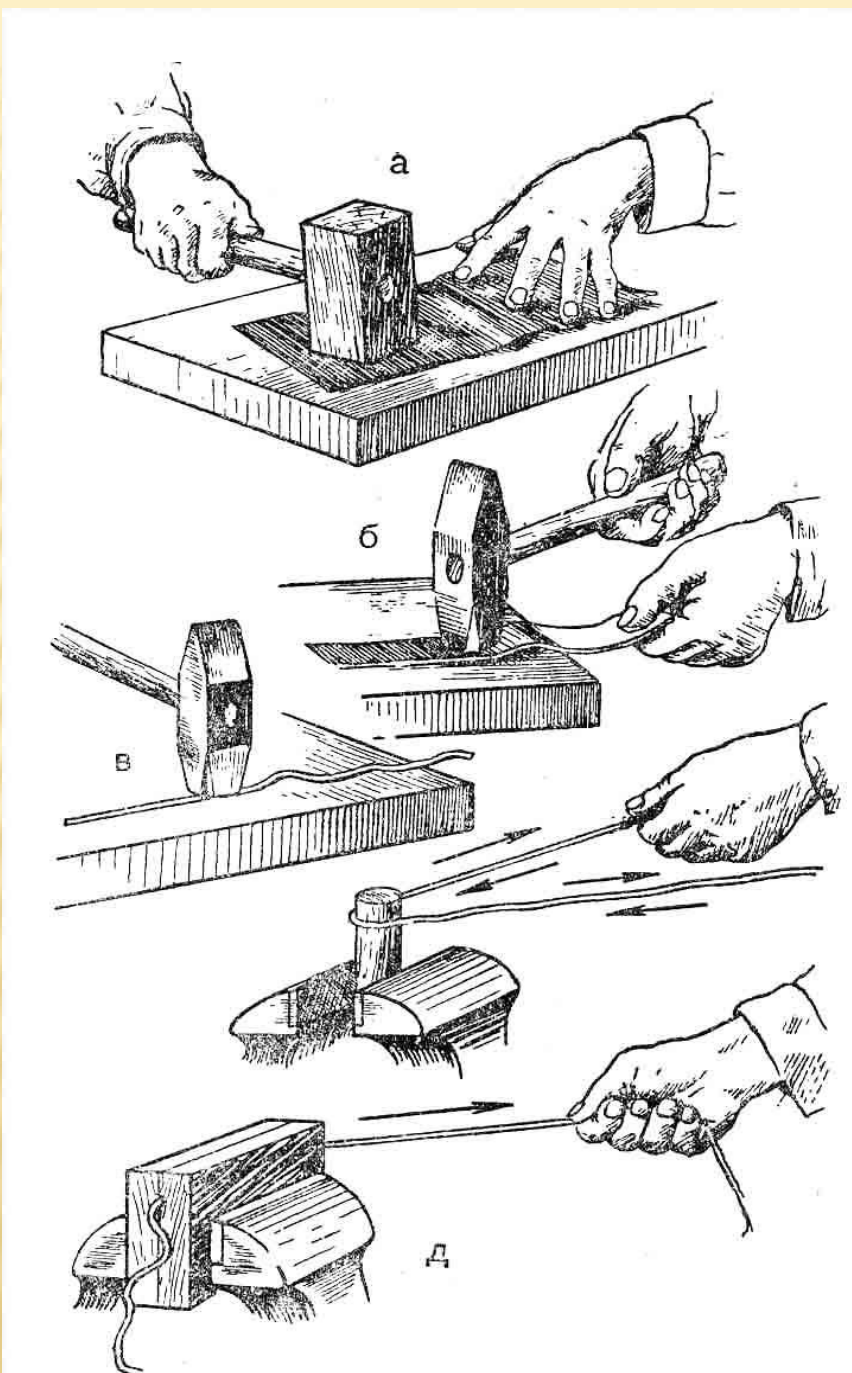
Провка (выпрямление) металла: а - правка листового металла при помощи киянки; б - правка полосового металла; в - правка толстой проволоки; г - правка проволоки протягиванием; д - правка проволоки волочением между двумя зажатými в тиски дощечками
